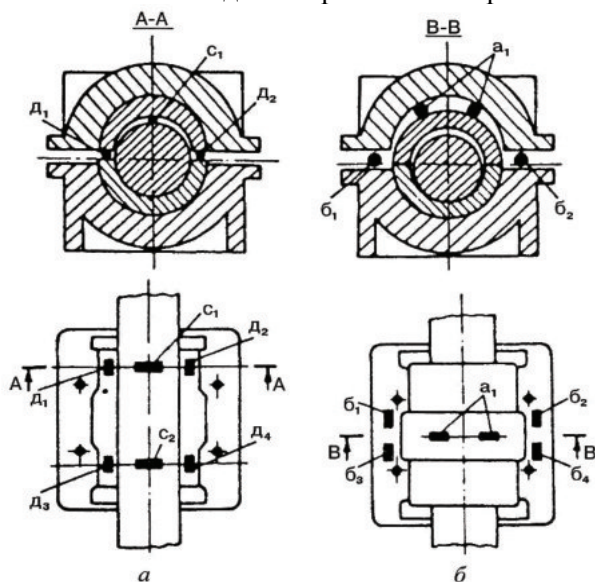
Контроль зазоров в подшипнике скольжения:
